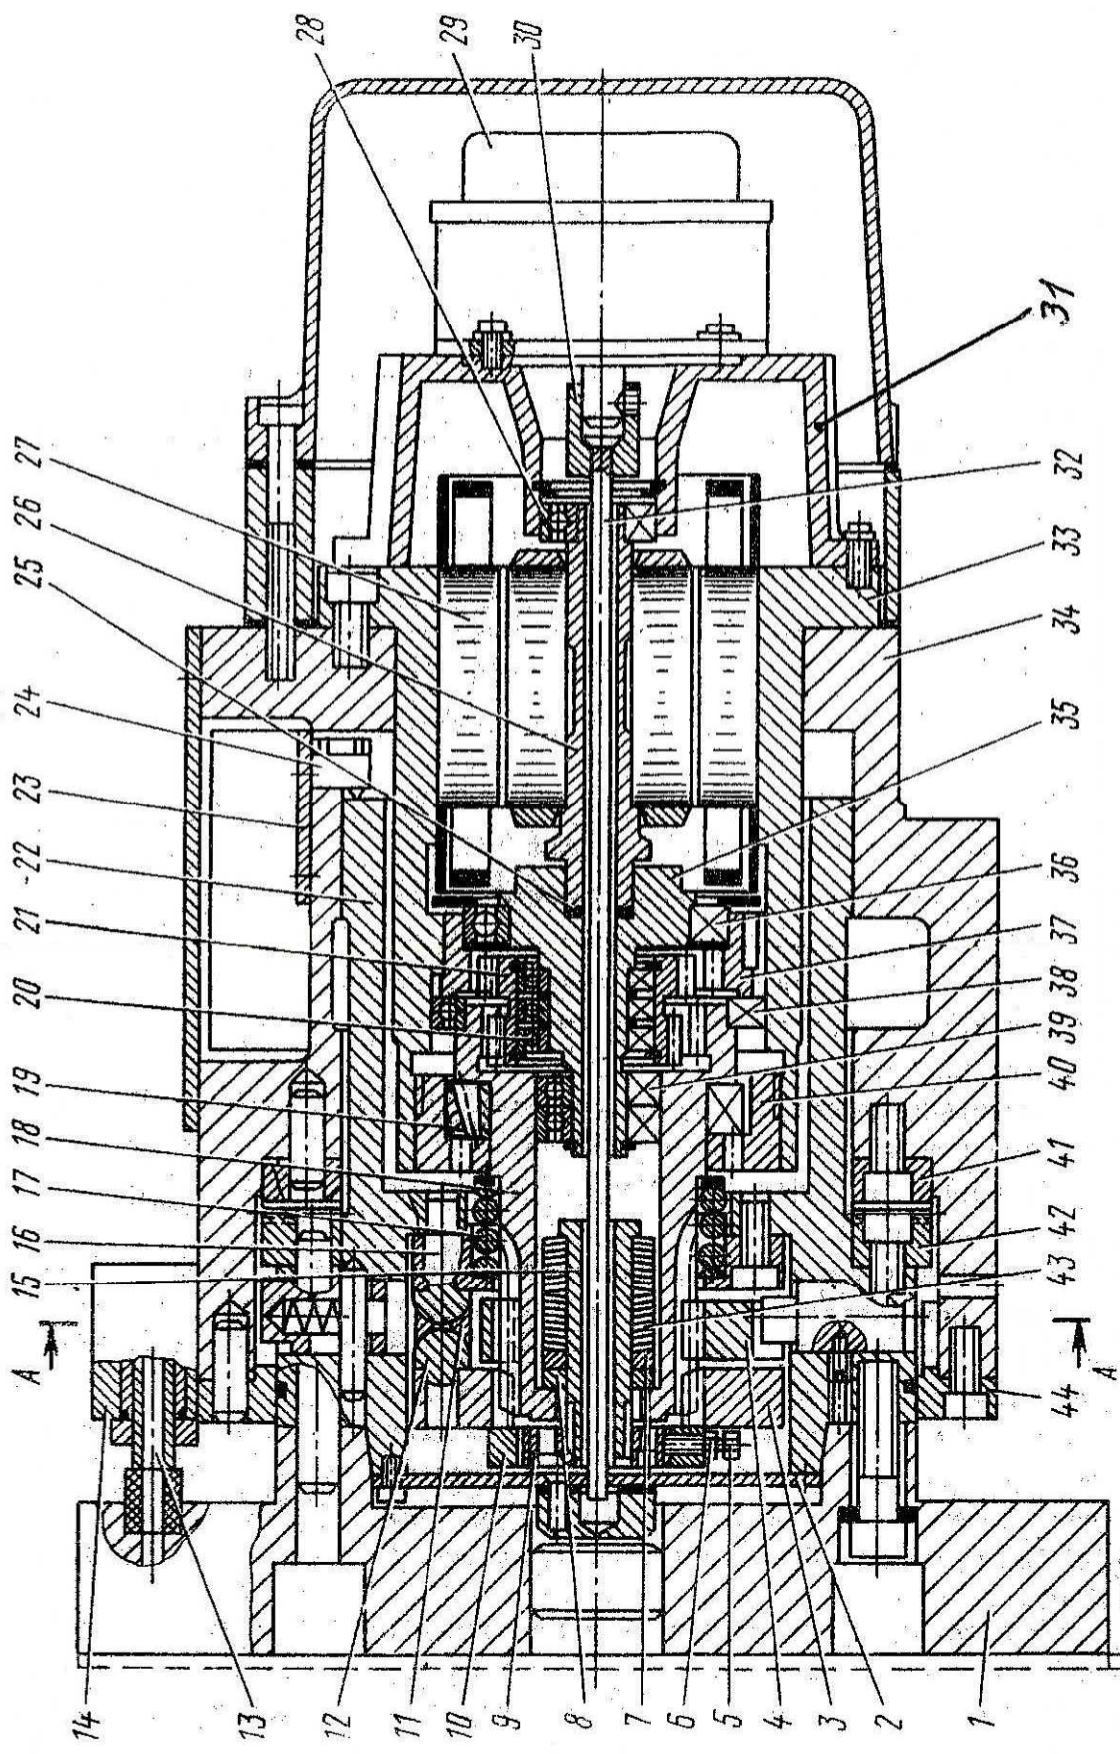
КОНСТРУКЦИЯ ГОЛОВКИ СВЕТОВОЙ
